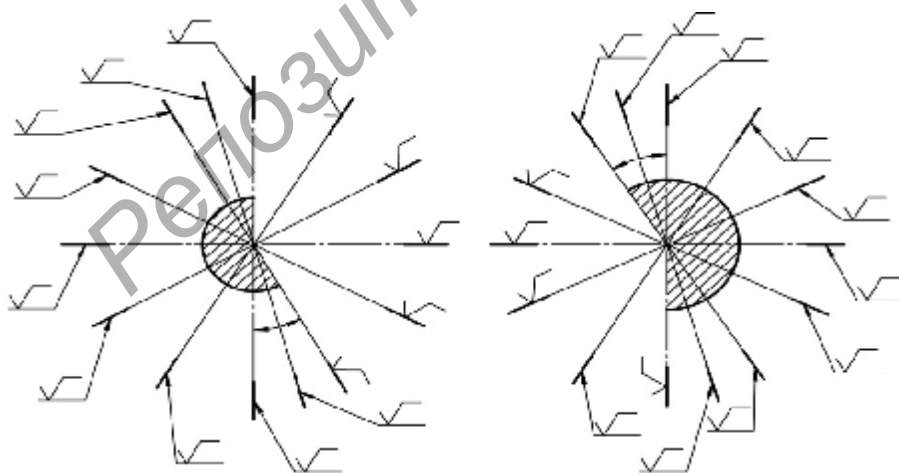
Нанесение знака шероховатости на поверхностях с различным расположением
